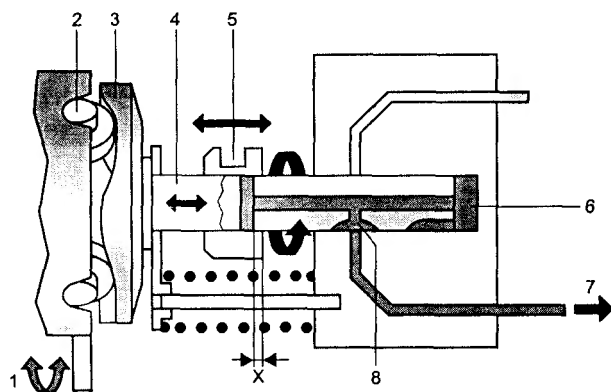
Система впрыска с распределительным аксиальным ТНВД: 1 — траектория поворота роликового кольца; 2 — ролик; 3 — кулачковая шайба; 4 — аксиальный плунжер-распределитель; 5 — регулирующая втулка; 6 — камера высокого давления; 7 — подача топлива к форсунке; 8 — распределительный паз; X — активный ход плунжера
